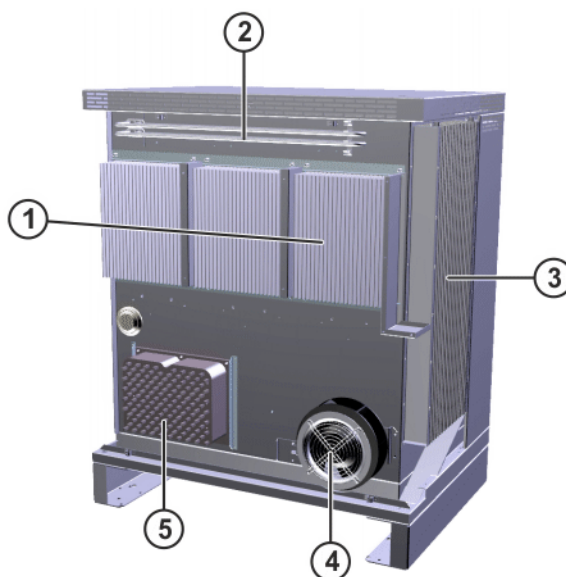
Aperçu de la commande de robot, vue arrière
